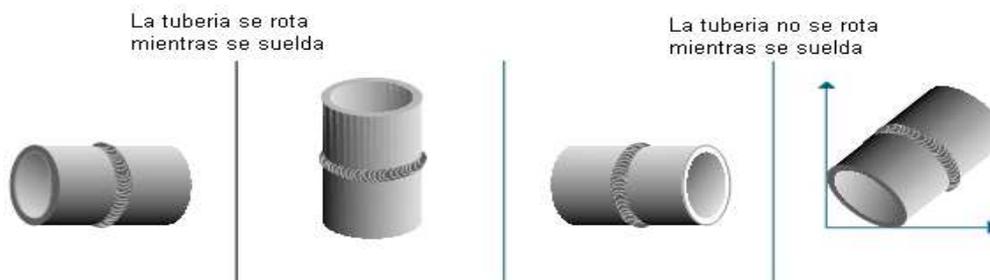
Posiciones de Soldadura de Filete
